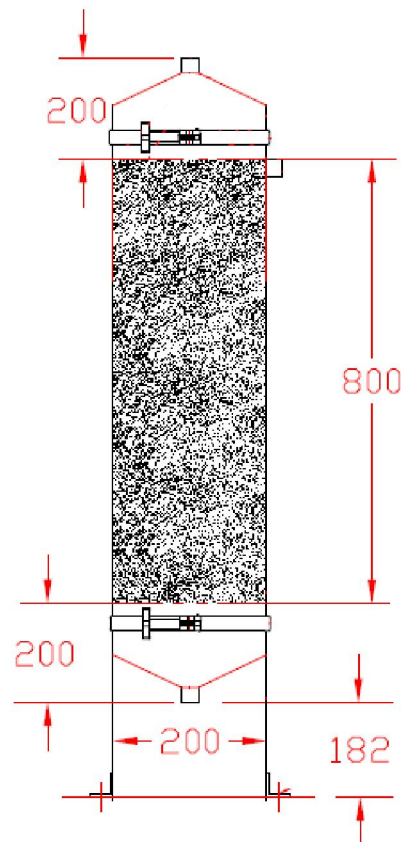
Diagrama de la columna proyectada (dimensiones en mm)
